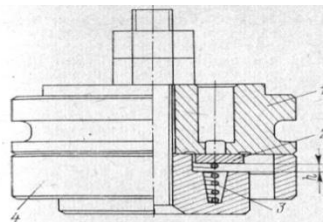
Клапан всасывающий кольцевой пластинчатый четвертой ступени.
